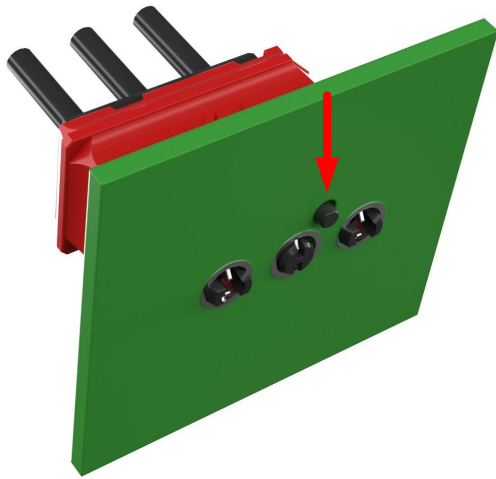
Kunststoffpin verhindert verdrehtes Stecken
